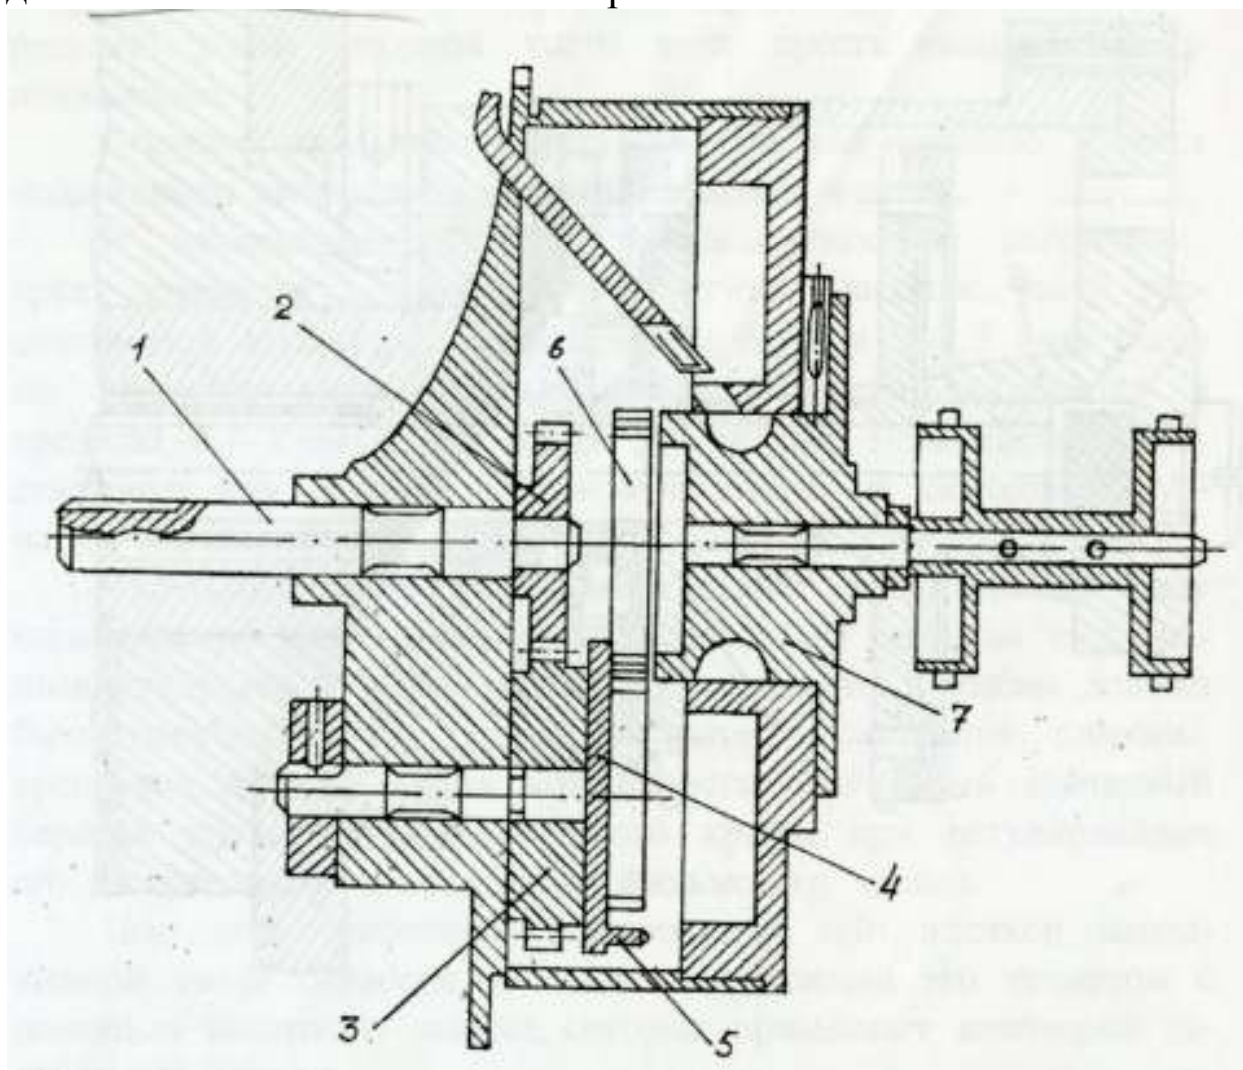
Конструкция мальтийского механизма с креплением скачкового барабана при помощи двух штифтов:
